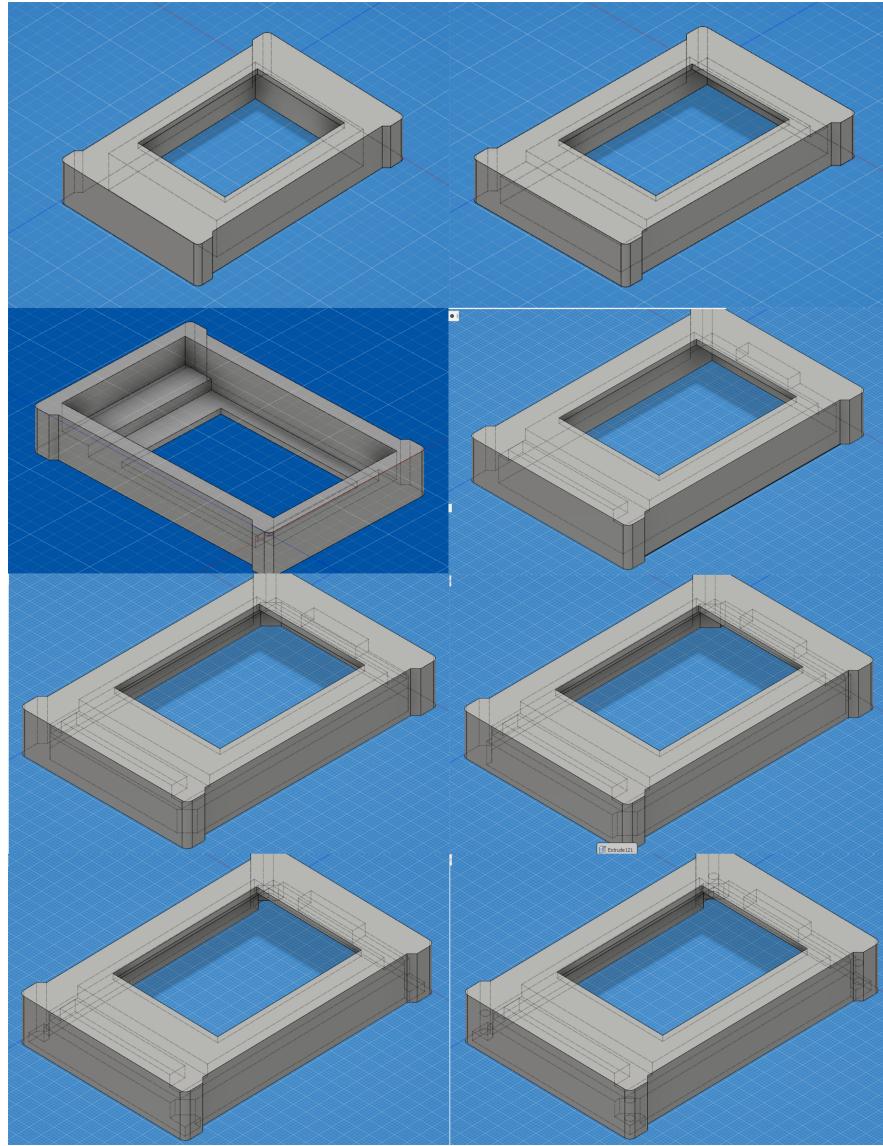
Proceso del Diseño del Molde Superior Parte 1
